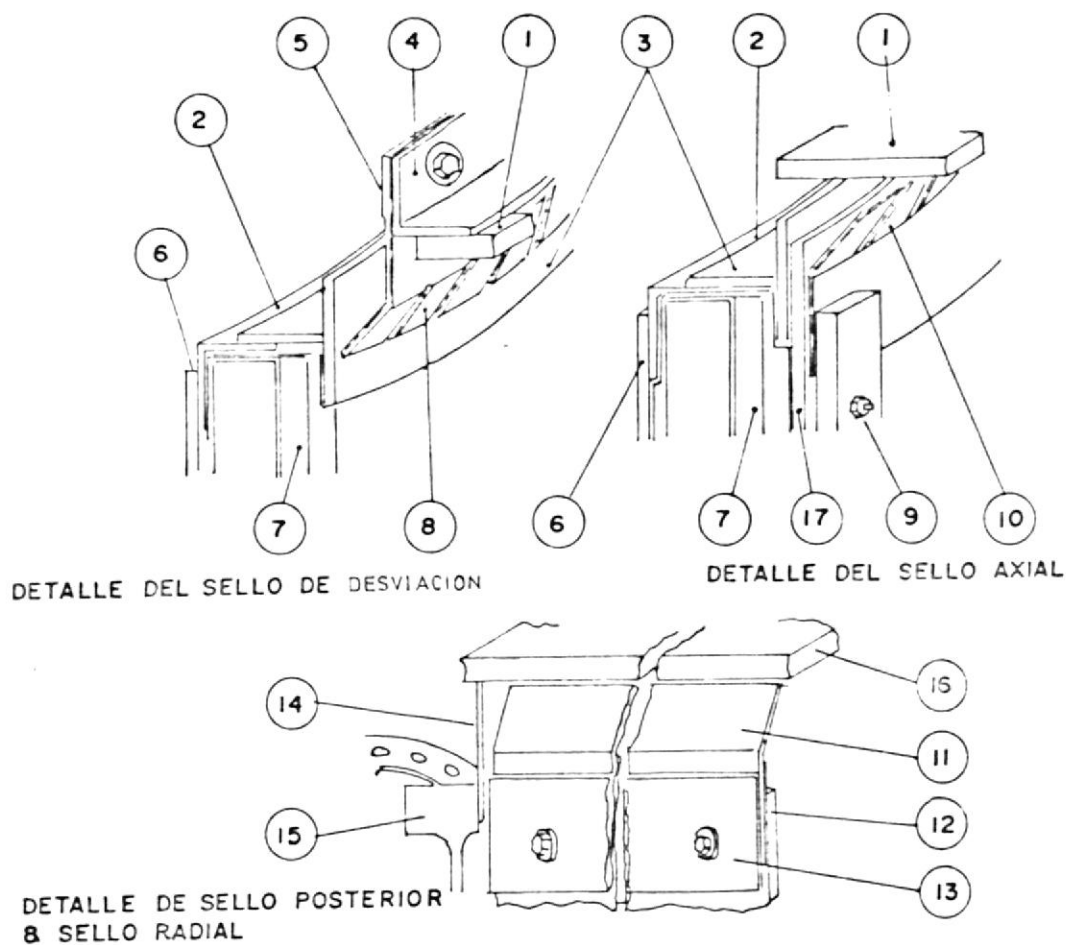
MONTAJE DE SELLOS DEL ROTOR
